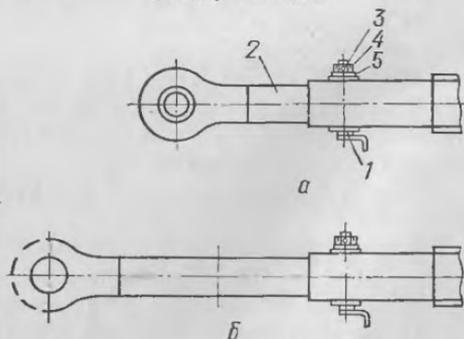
Установка колес опрыскивателя ОП-2000-2-01.
